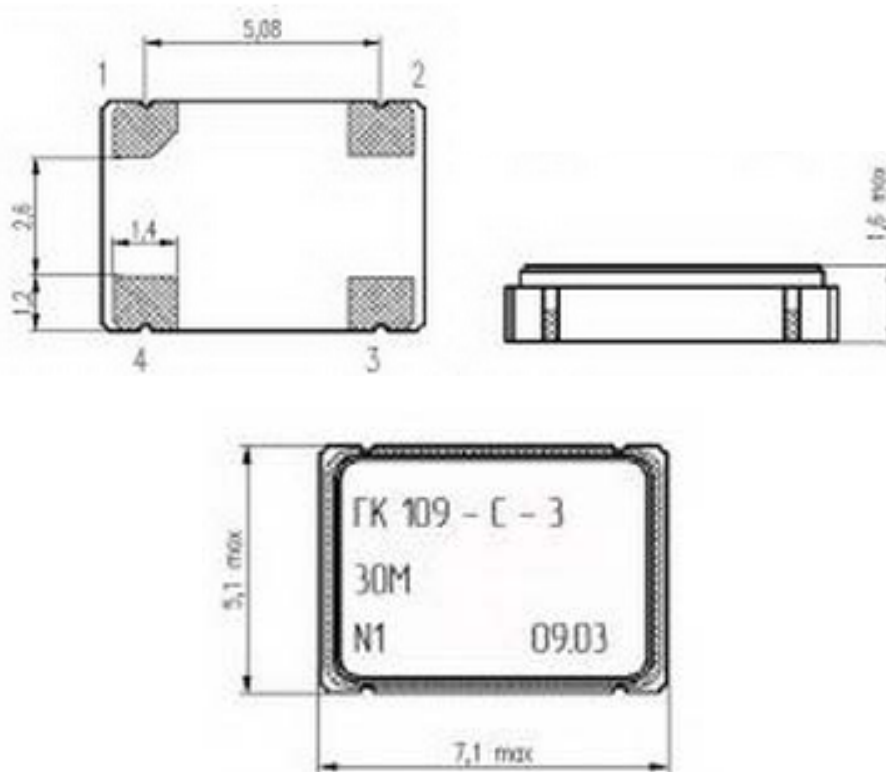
Габаритные, установочные и присоединительные размеры генератора ГК-109С
